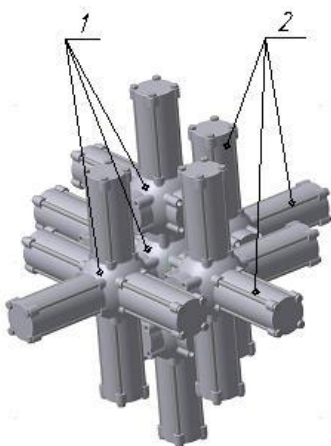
Багатокамерний вибухоударний модульний контейнер з гніздовим (радіальним) розташуванням вибухоударних модулів: 1 – вибухова камера; 2 – ударні циліндри
